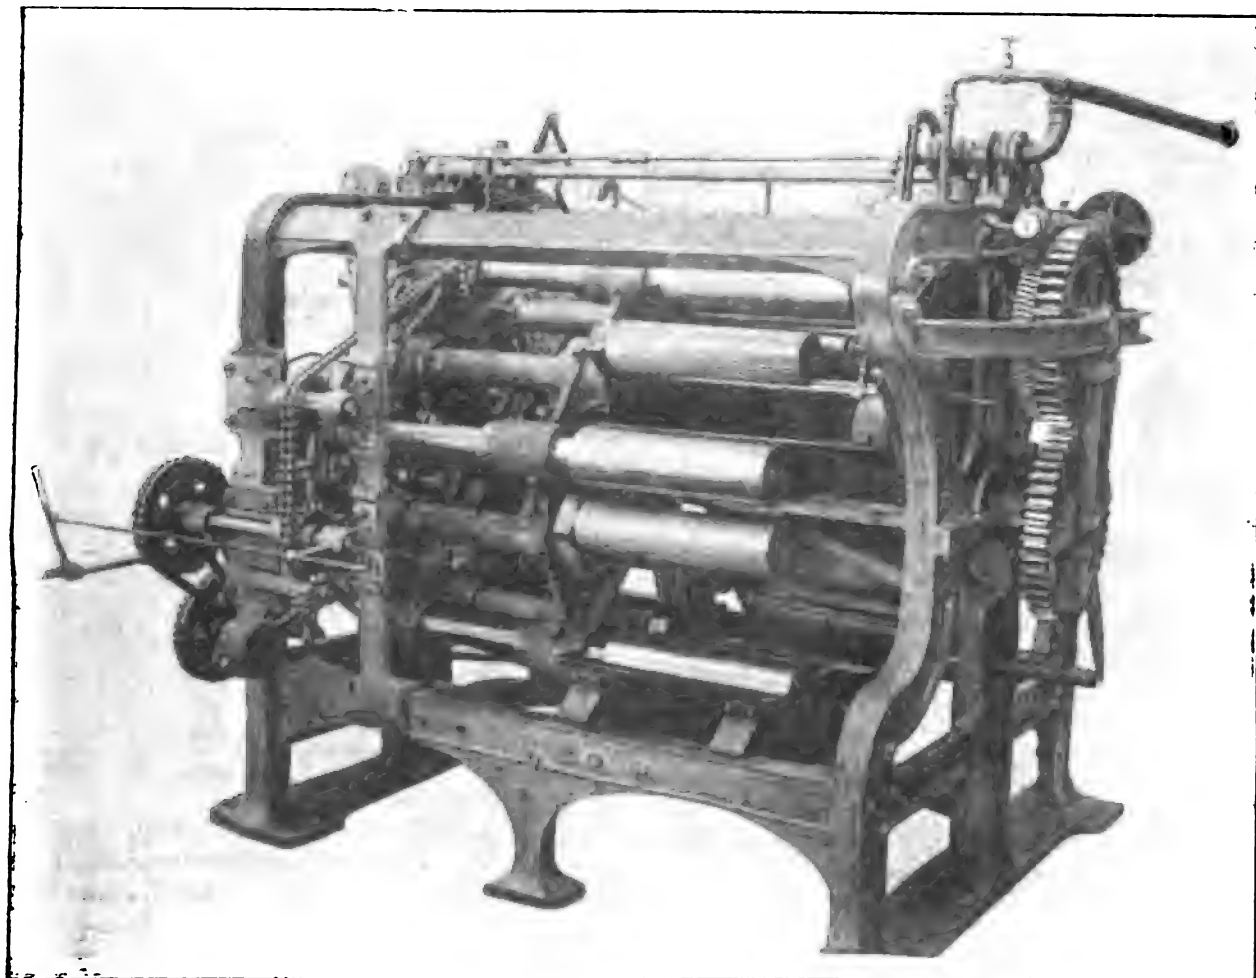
Machine à merceriser type revolver (Dolder).
